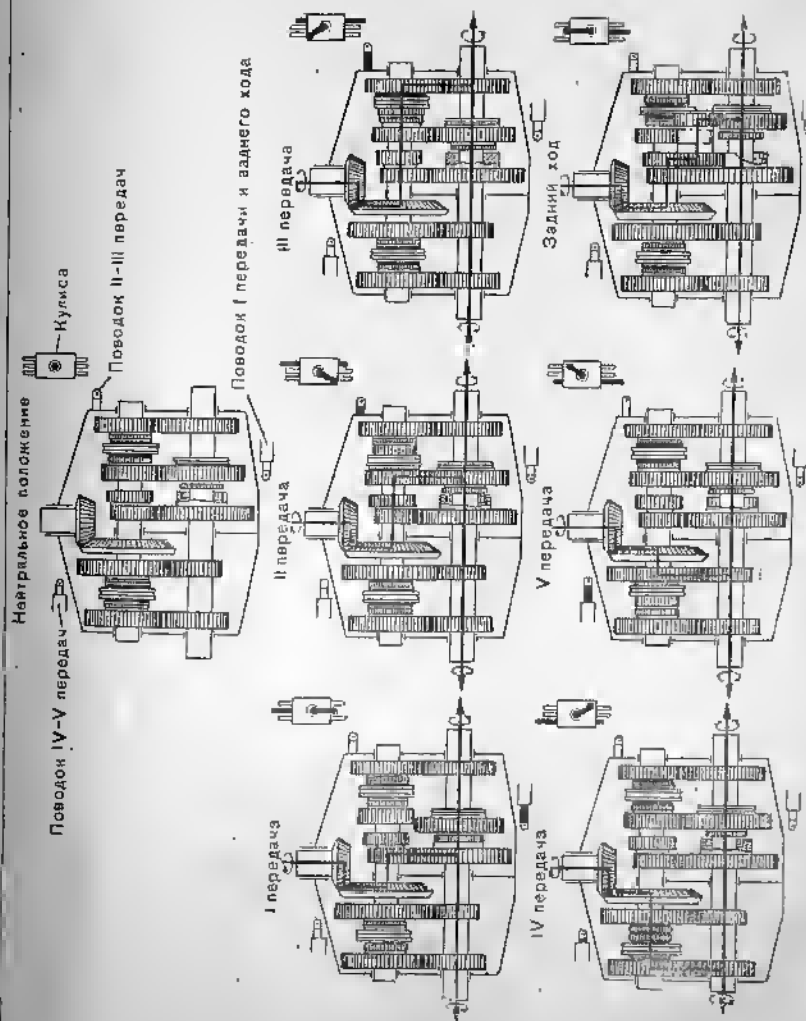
Схема включения шестерен коробки передач на всех передачах
